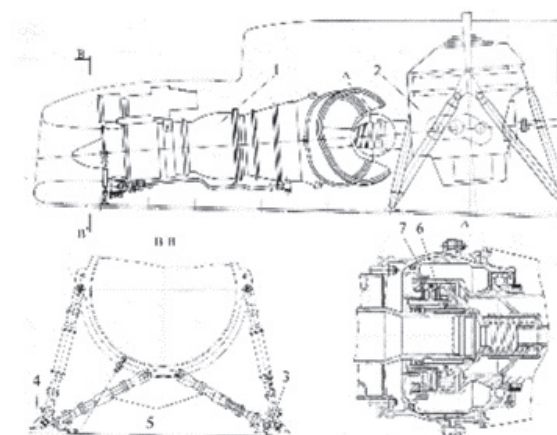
Конструкция крепления двигателя с шаровой опорой на главном редукторе.
